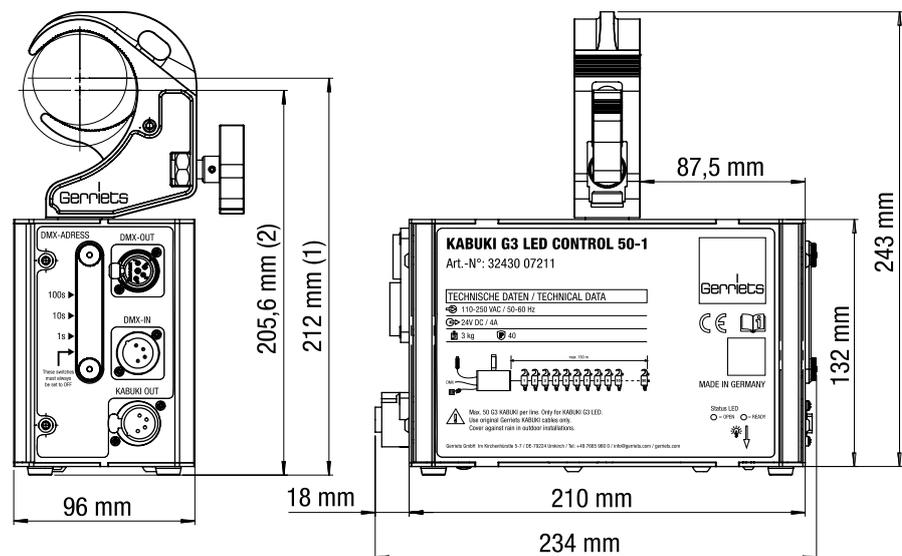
Maße – Steuerung KABUKI G3 50-1 LED (links: Frontansicht mit Anschlüssen; rechts Seitenansicht)
